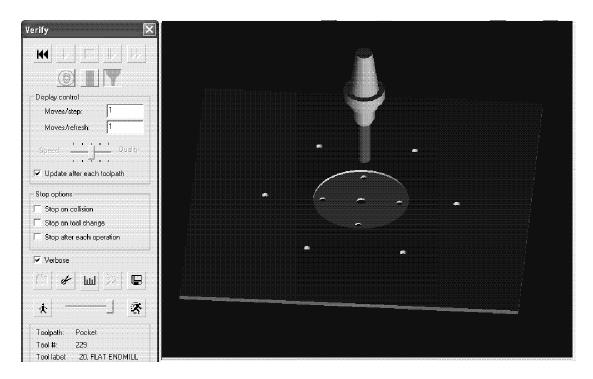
Maquinado de caja en la pieza con Pocket Toolpath
